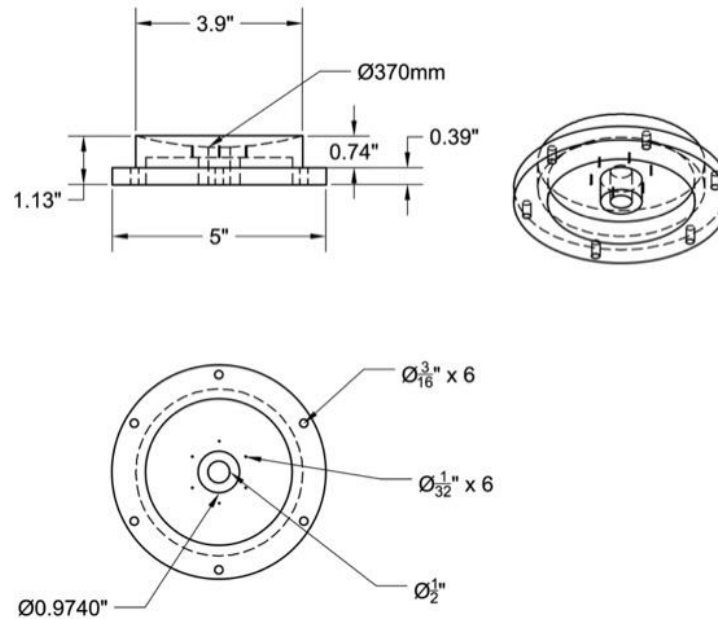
Diseño de la copa y brida: dimensiones.
